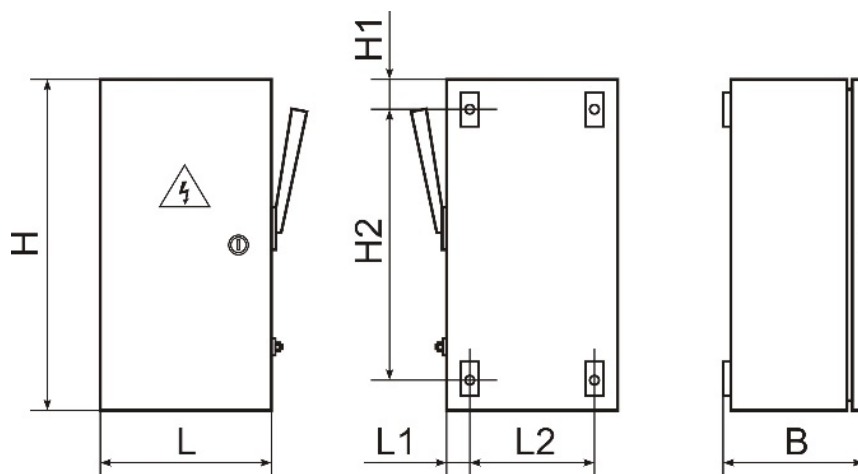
Общий вид и габаритные размеры ящиков силовых ЯРП
